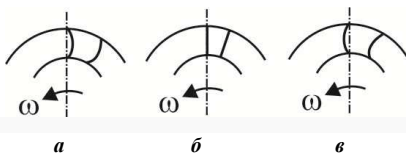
Типи лопаток робочого колеса компресора: а – загнута вперед; б – радіальна; в – загнута назад [29]
